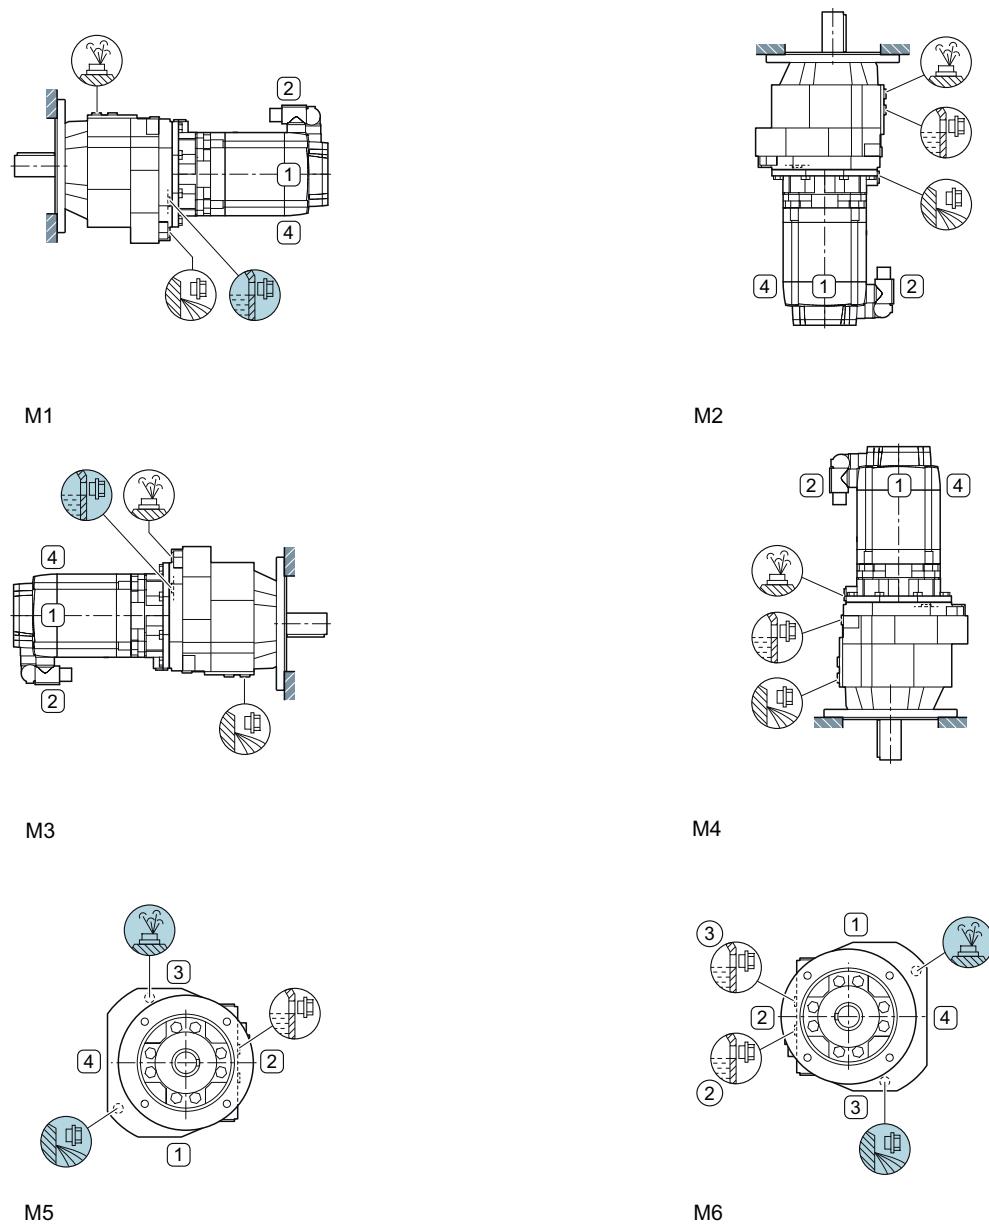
Einbaulagen für Servo-Stirnradgetriebemotoren DF und ZF (Flanschausführung) oder DZ und ZZ (Gehäuseflanschausführung), Baugrößen 49 - 129, 2-stufig und 3-stufig
